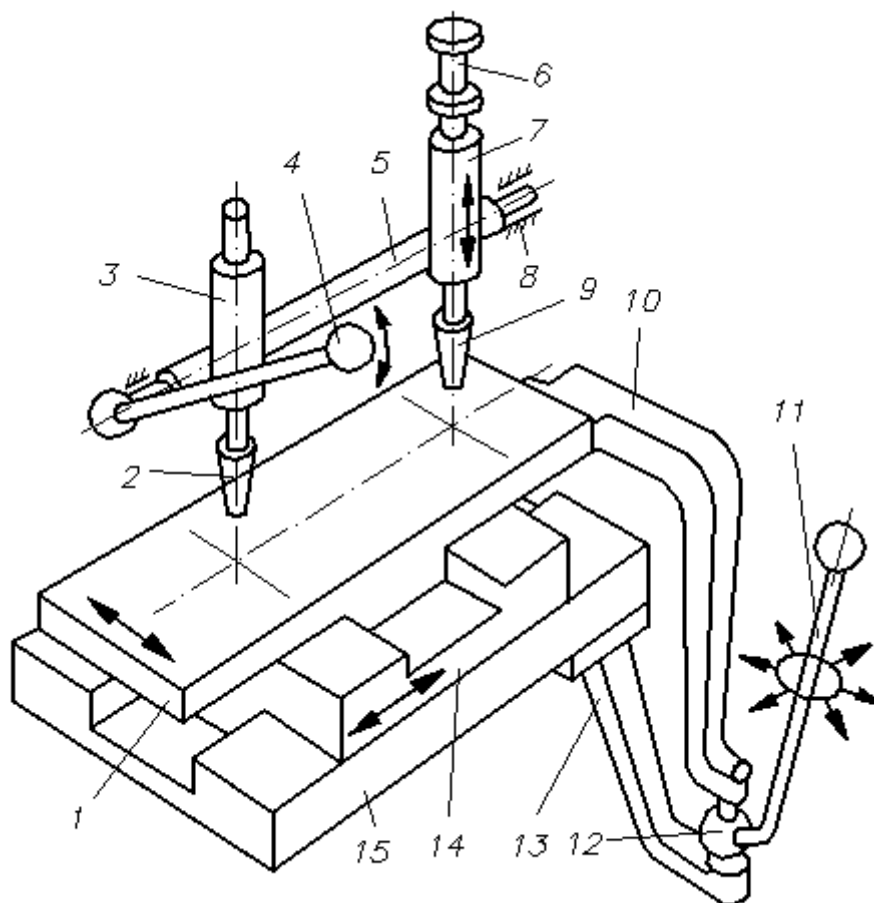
Копіювальний агрегат з управління двома руками
